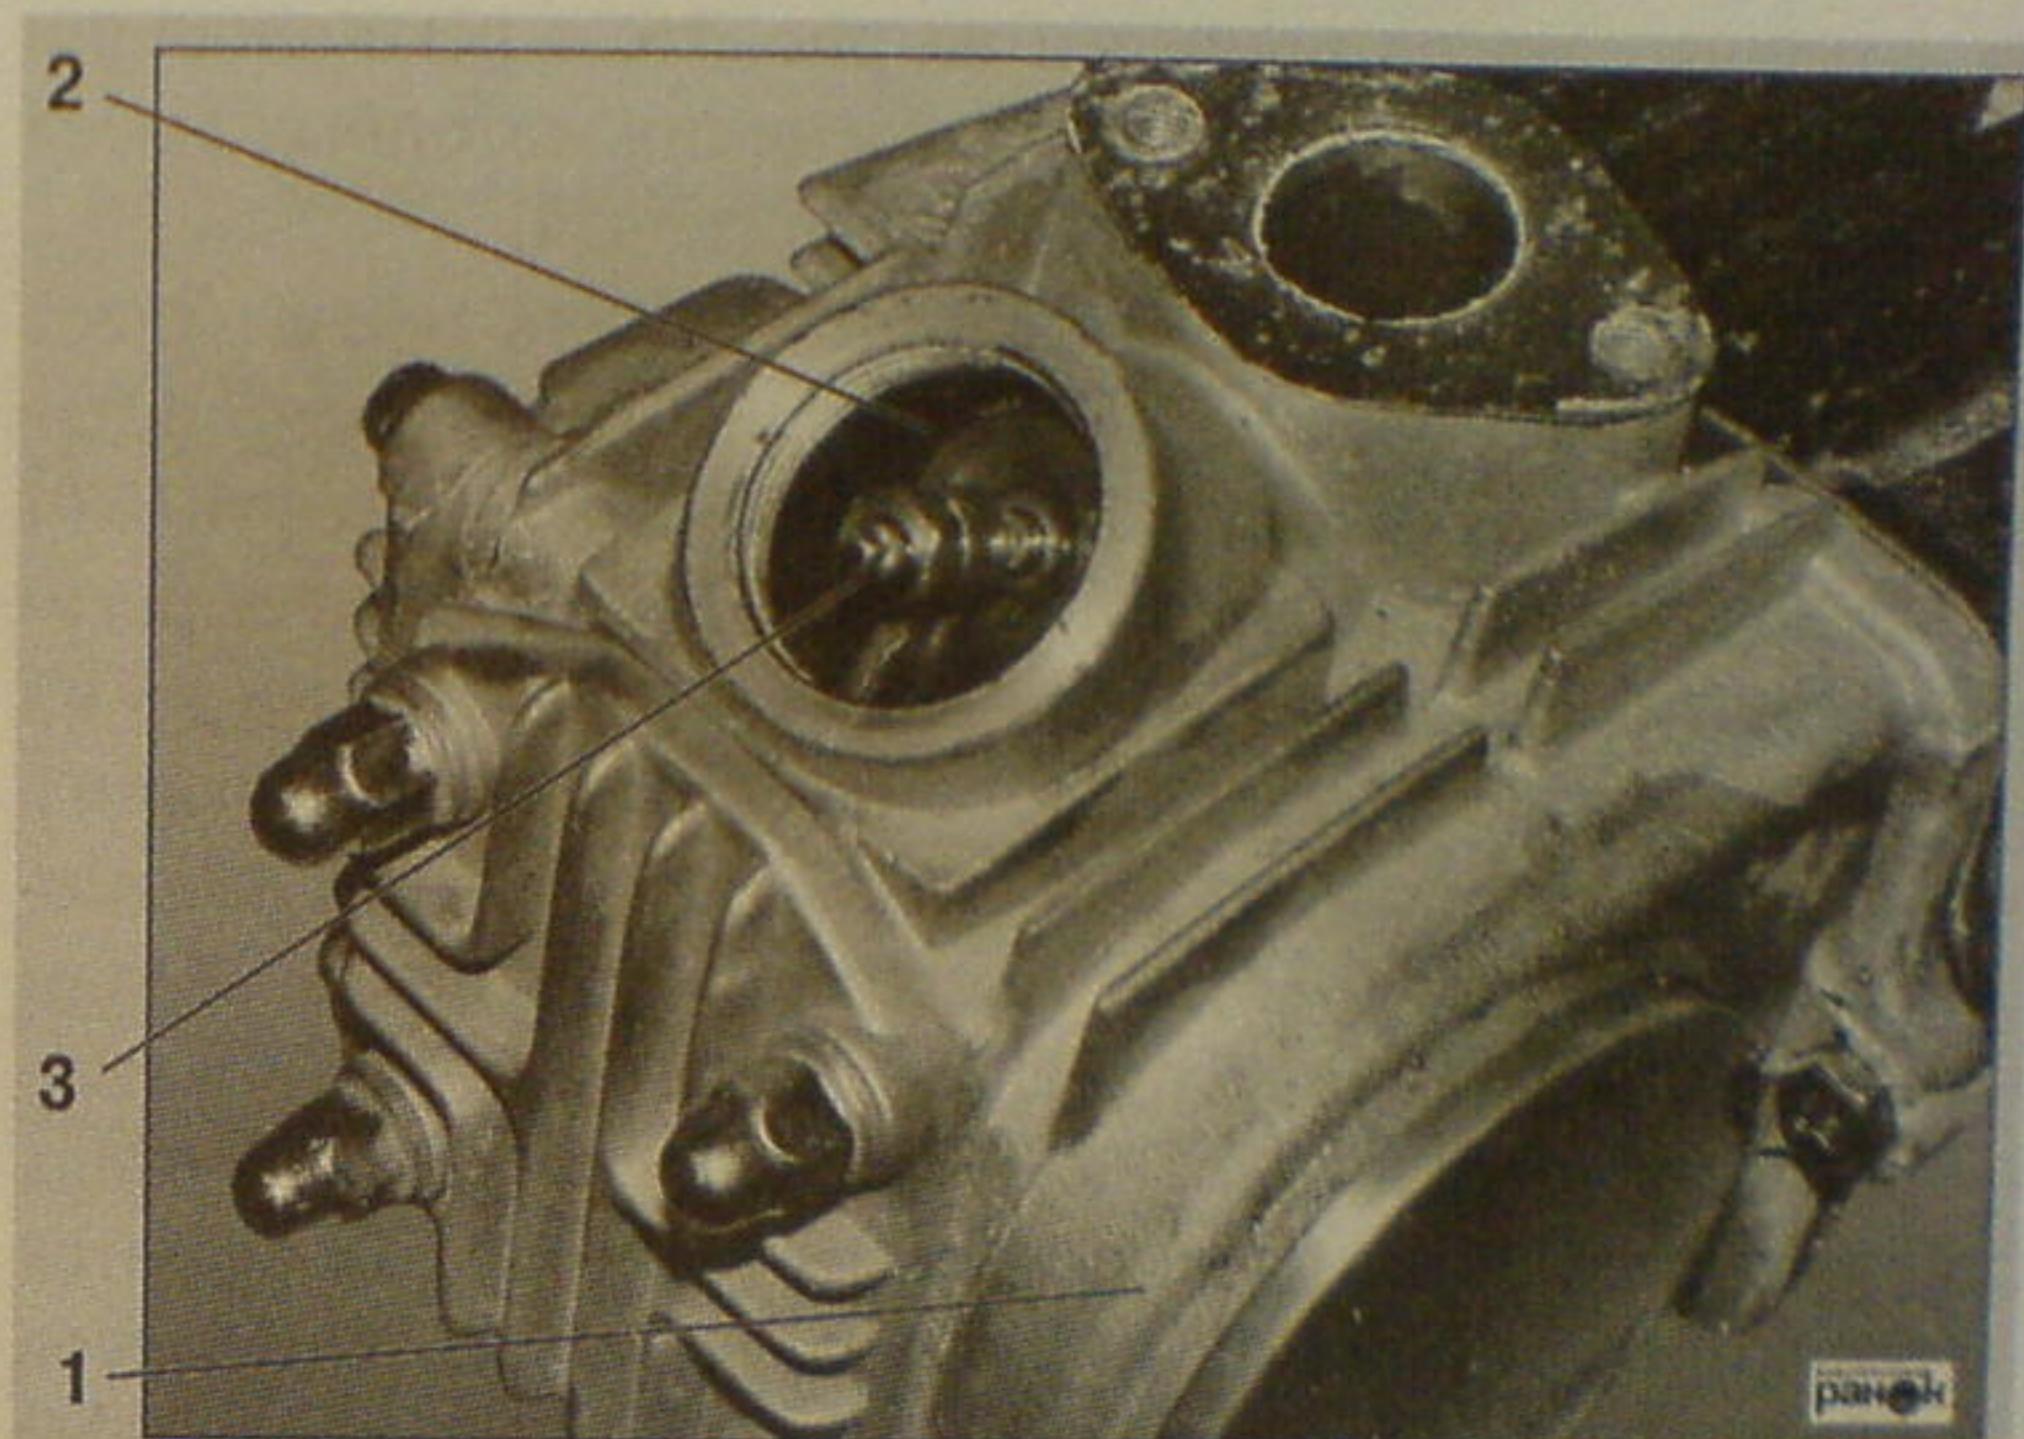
Расположение регулировочного винта зазоров клапанов: 1 – головка цилиндра; 2 – регулировочное отверстие; 3 – регулировочный винт
